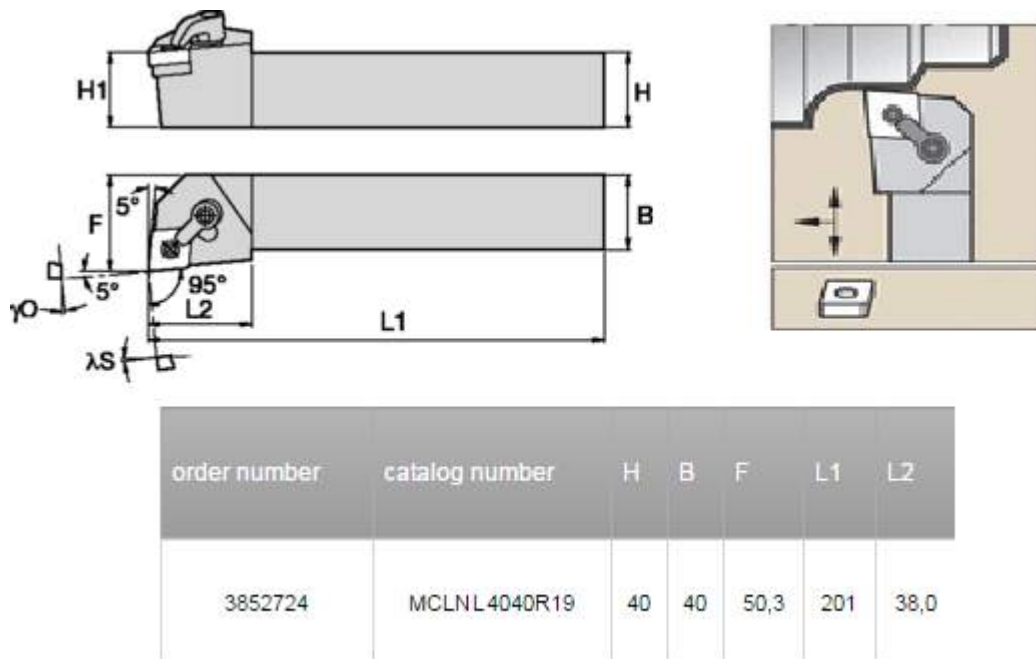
Габариты державки резца и пример обрабатываемы поверхностей
